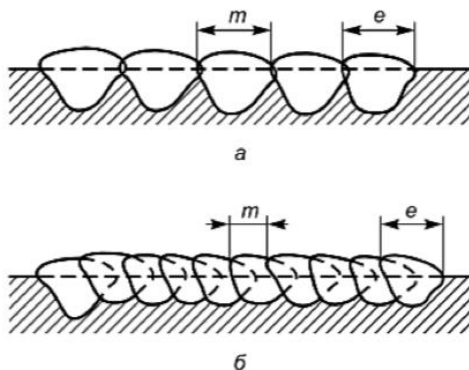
Схема наплавки валиков при разной величине шага наплавки:
